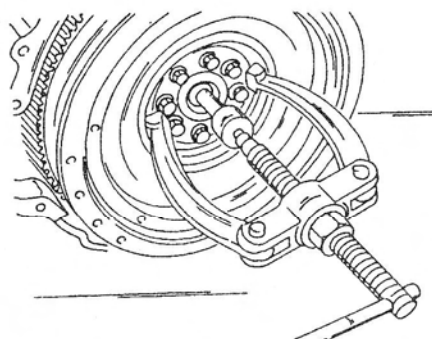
При снятии шарикового подшипника коленчатого вала маховик должен быть закреплен болтами.
